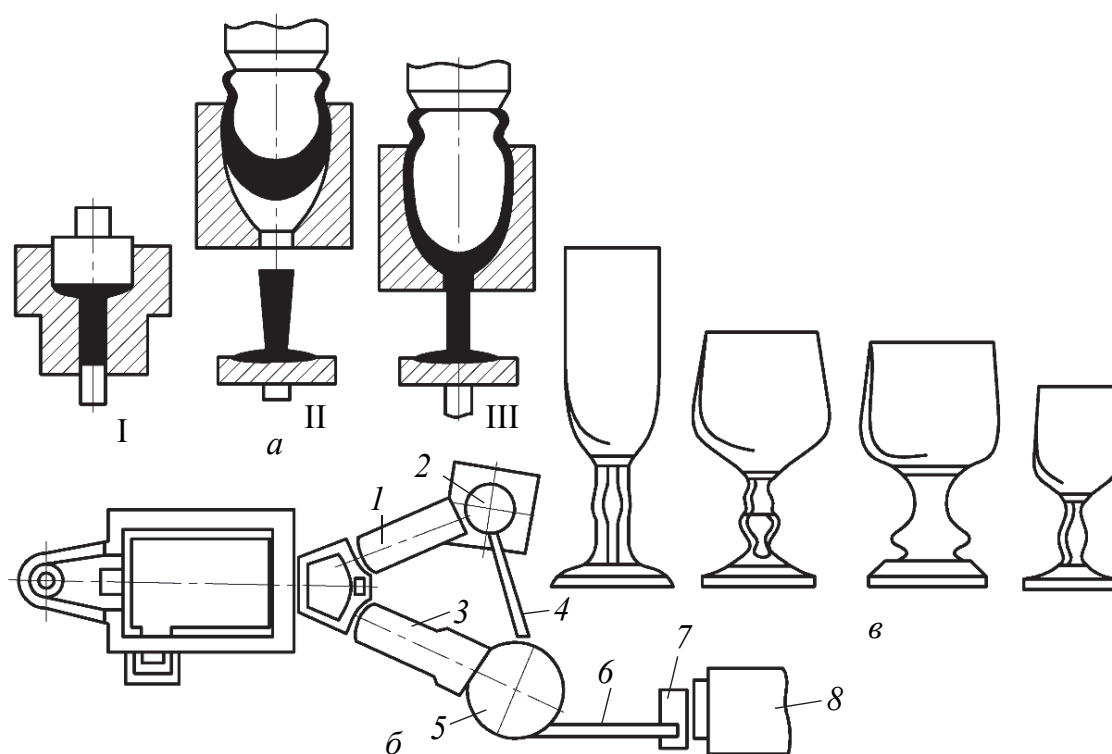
Схемы изготовления изделий на ножке (а), технологической линии (б) и виды вырабатываемых изделий (в); 1 – питатель; 2 – форма прессы; 3 – конвейер; 4 – формы выдувного автомата; 5 – питатель; 6 – конвейер; 7 – загрузчик; 8 – печь отжига
